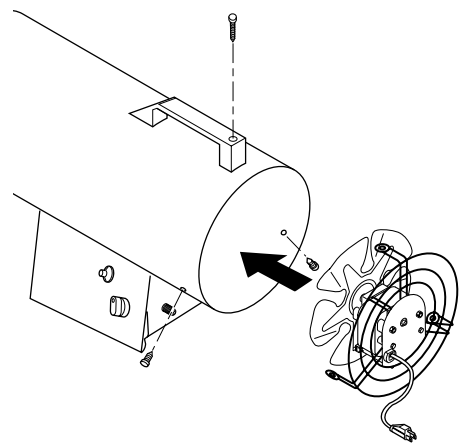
Remise en place du moteur et de la grille du ventilateur
